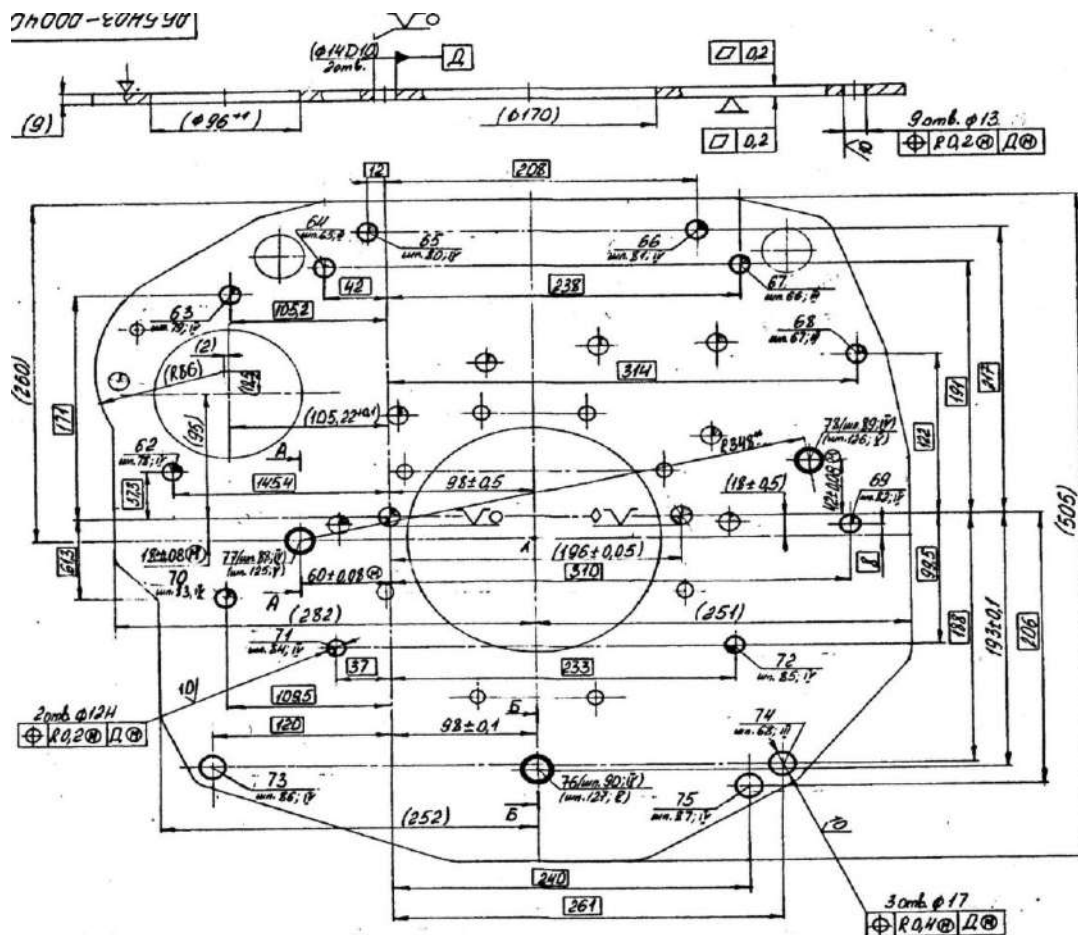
Представитель из шести деталей, обрабатываемых на агрегатном станке
